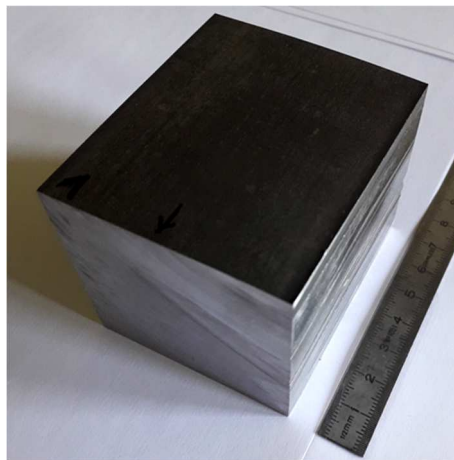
Photographie du lopin assemblé par soudage diffusion par CIC après retrait du conteneur
